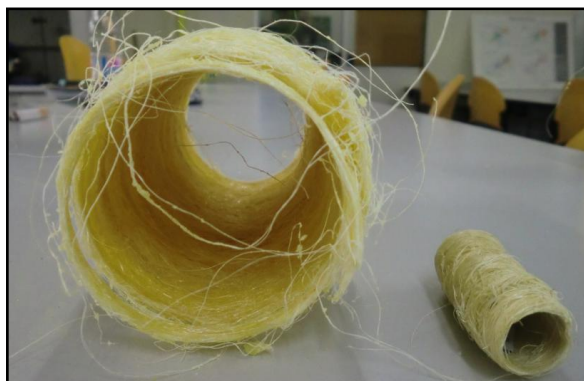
À esquerda, tubo enrolado mecanicamente, à direita tubo enrolado manualmente
